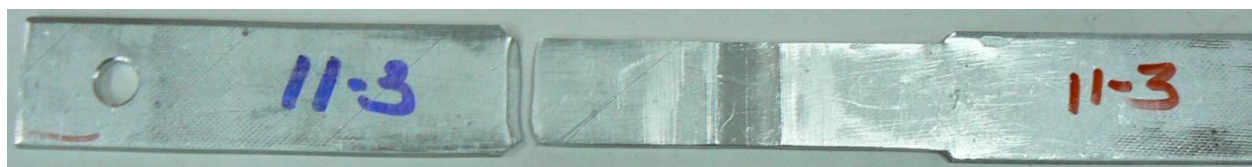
Картина разрушения образца толщиной 4 с соединением, полученным сваркой трением с перемешиванием
